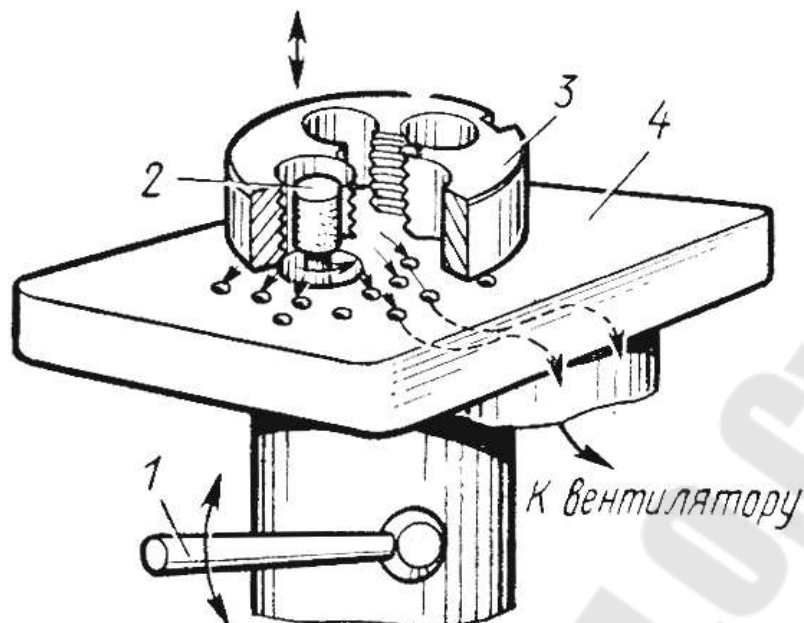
Эскиз общего вида станка модели МФ-27А для заточки плашек:
